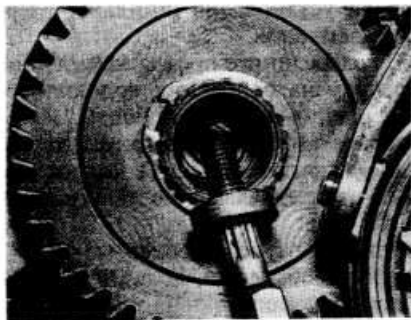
Отверните болт с торцевой части ведущего вала
